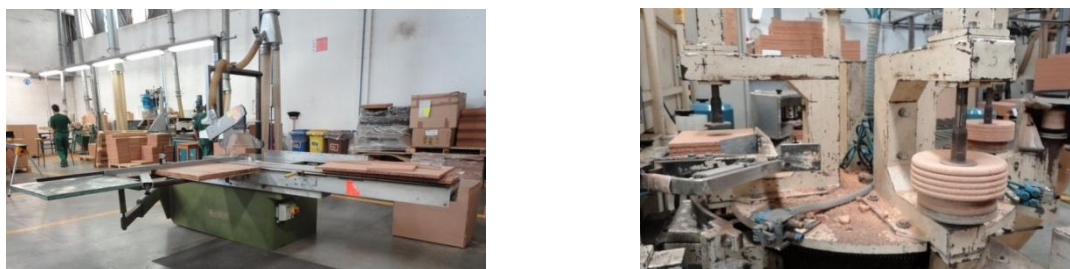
Serra de disco utilizada no corte de placas (à esquerda) e fresagem para conferir a forma final (à direita).
